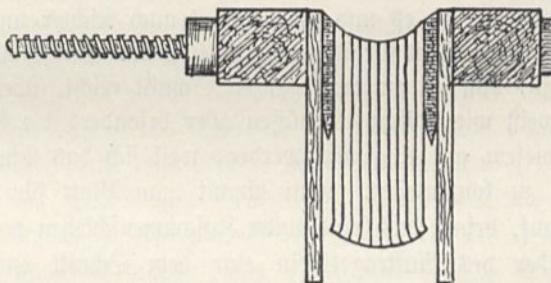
Enggepreßtes Buch zu Hohlgoldschnitt.
